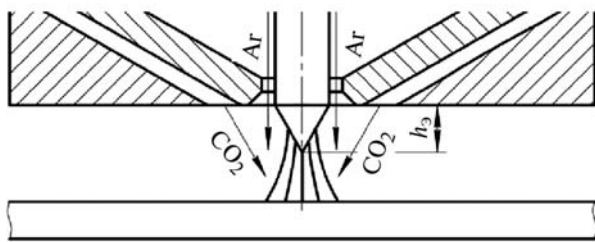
Схема горелки для сварки неплавящимся электродом с комбинированной защитой
